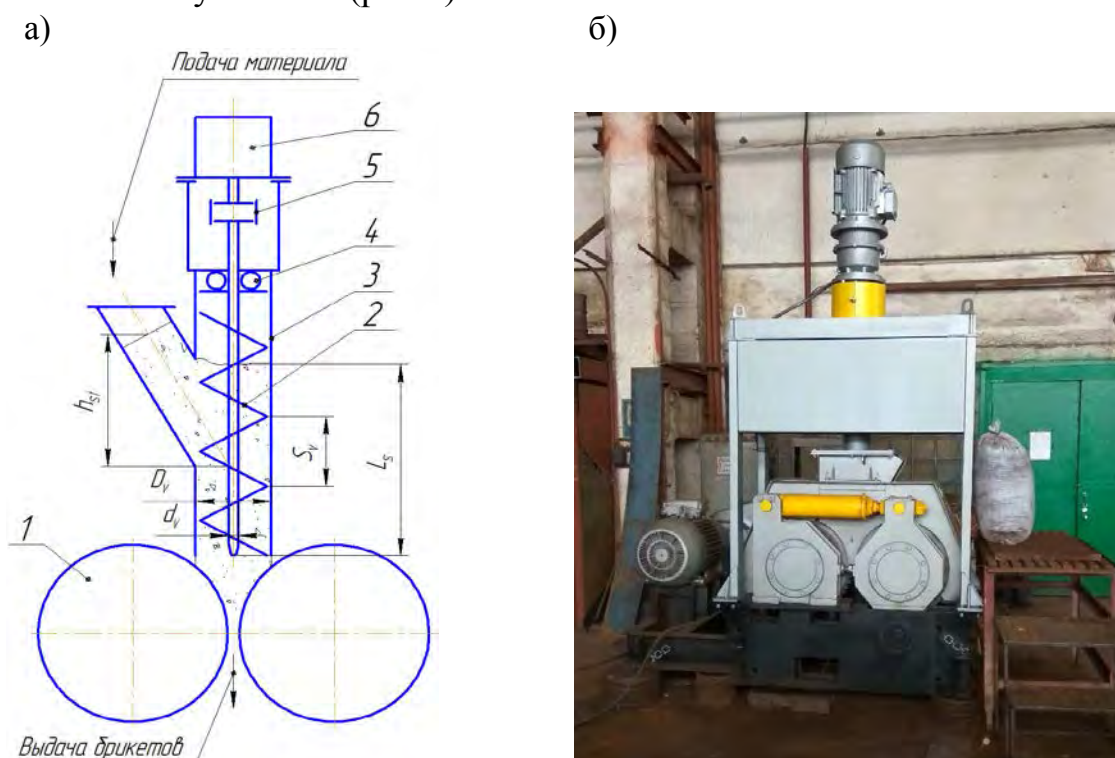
Валковый пресс конструкции ИЧМ, оснащенный подпрессовщиком:
